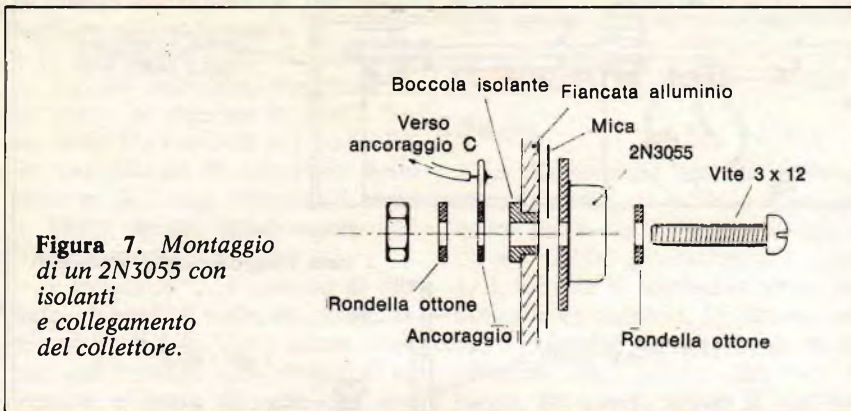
Montaggio di un 2N3055 con isolanti e collegamento del collettore.
